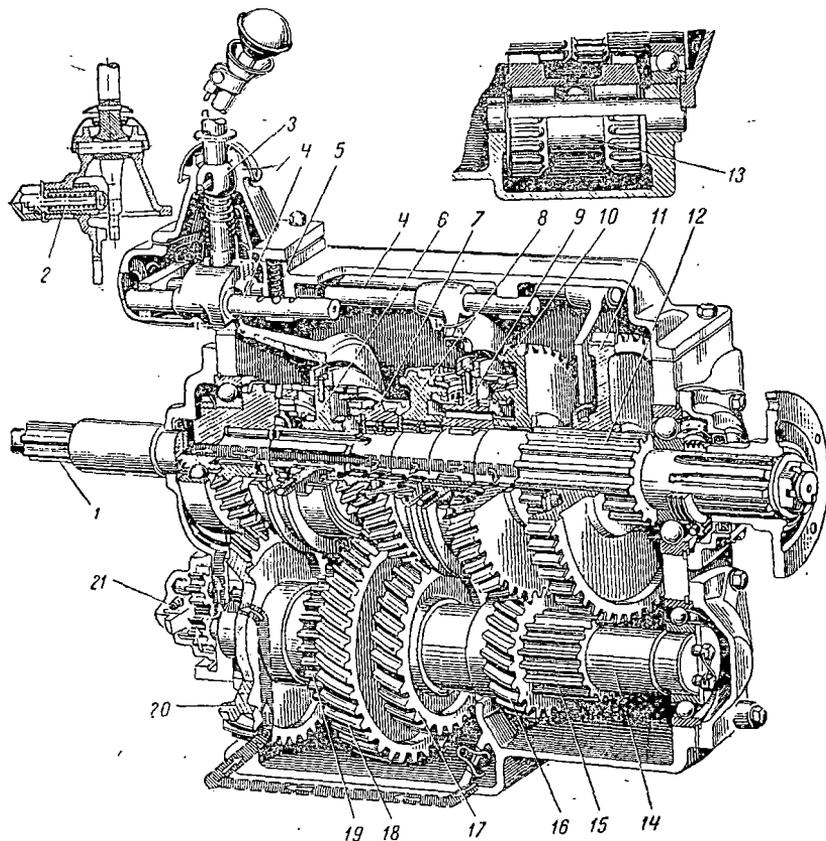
Коробка передач автомобилей МАЗ-200, КраЗ-219 и Урал-375:
